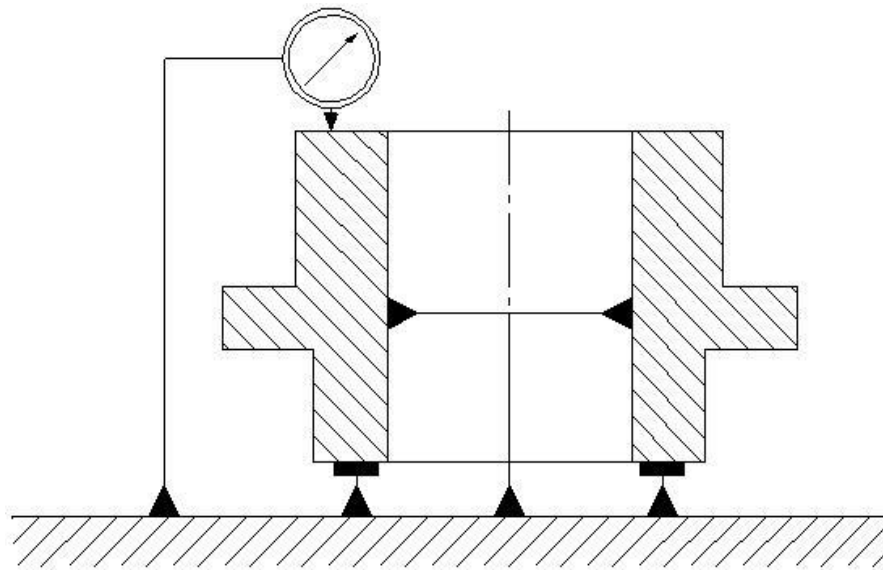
Ескіз схеми контролю торцевого биття відносно внутрішньої циліндричної поверхні.
